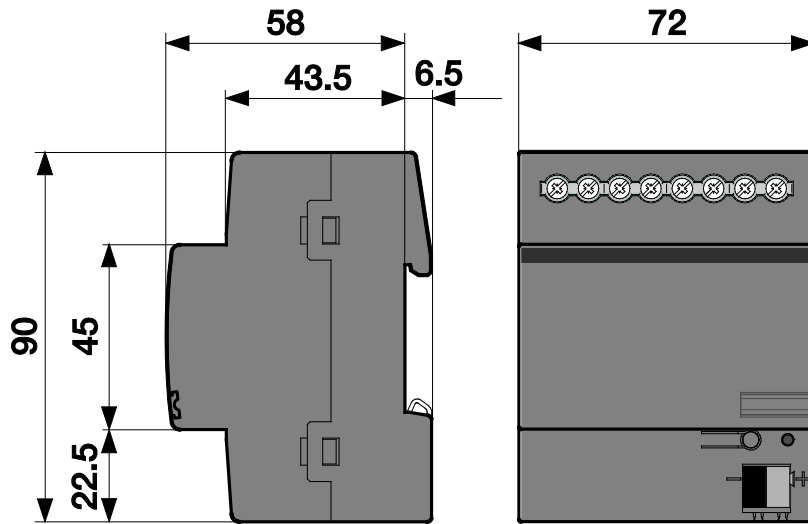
Dimensiones del actuador de calefacción de 6 canales
